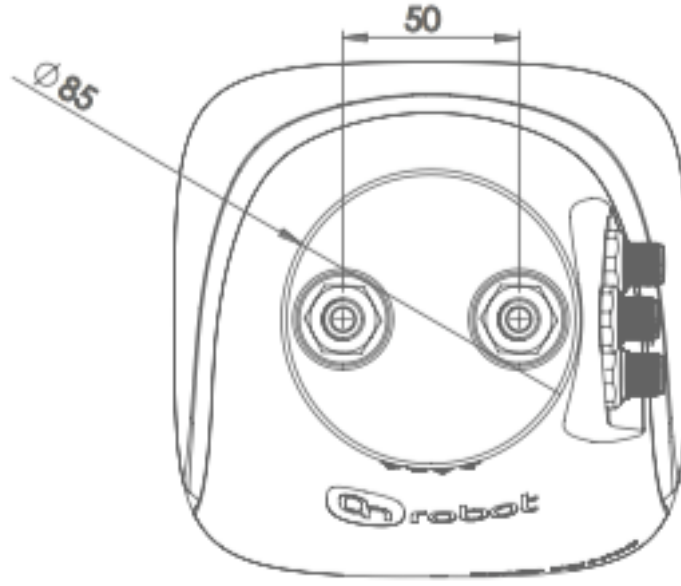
Gecko Tutucu ön ve yan boyutları.
